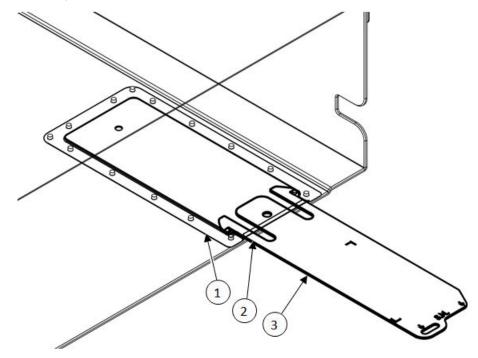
Servicetag (Komponenten zwecks besserer Übersichtlichkeit entfernt)
